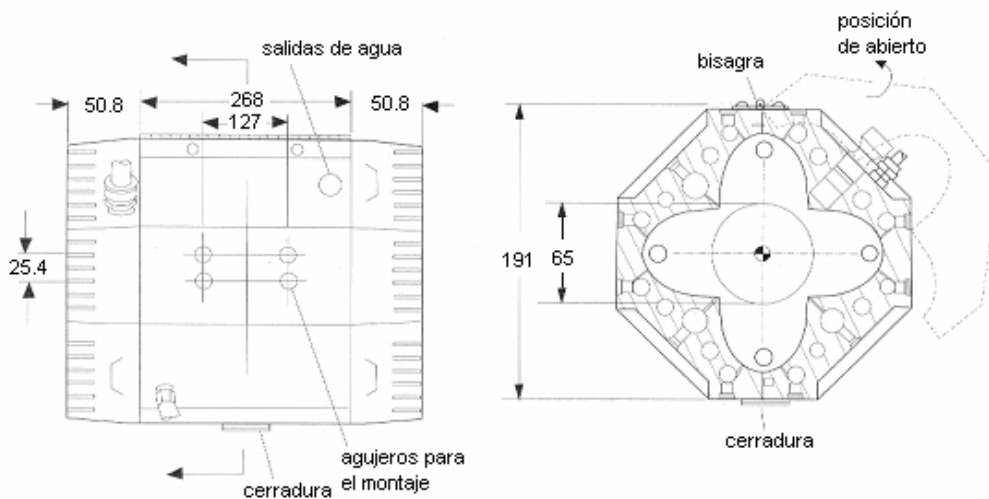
5 Geometría y dimensiones del horno en (mm)
